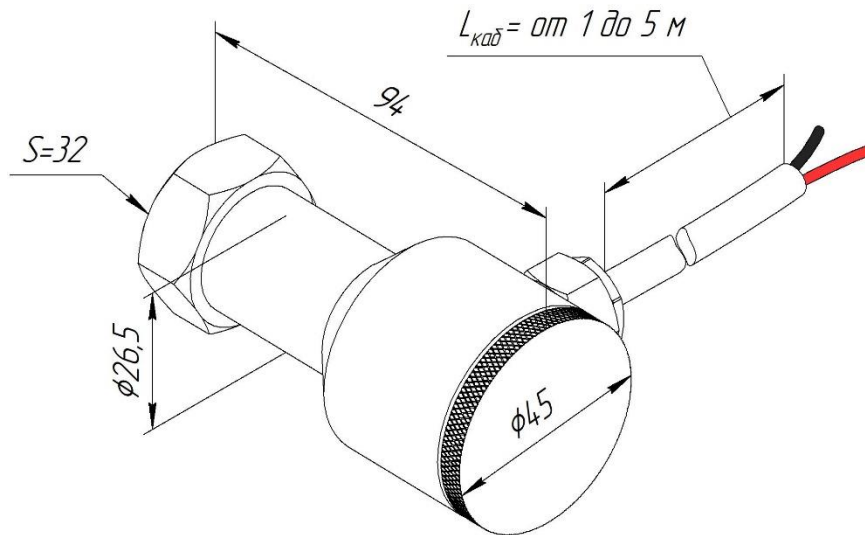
б. Общий вид фотодатчика ФД-105Т-Ех. Вид 2
